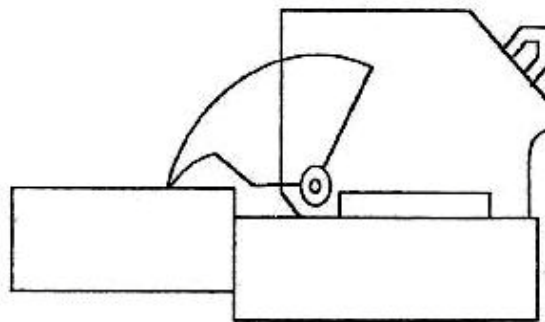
Evaluación del alineamiento en una junta a tope antes de ser soldada
